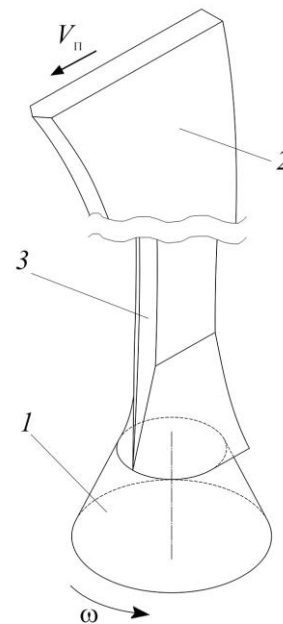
Загальний вигляд щілинно-фрезерного робочого органу: 1 – фреза; 2 – ніж; 3 – різальна кромка
